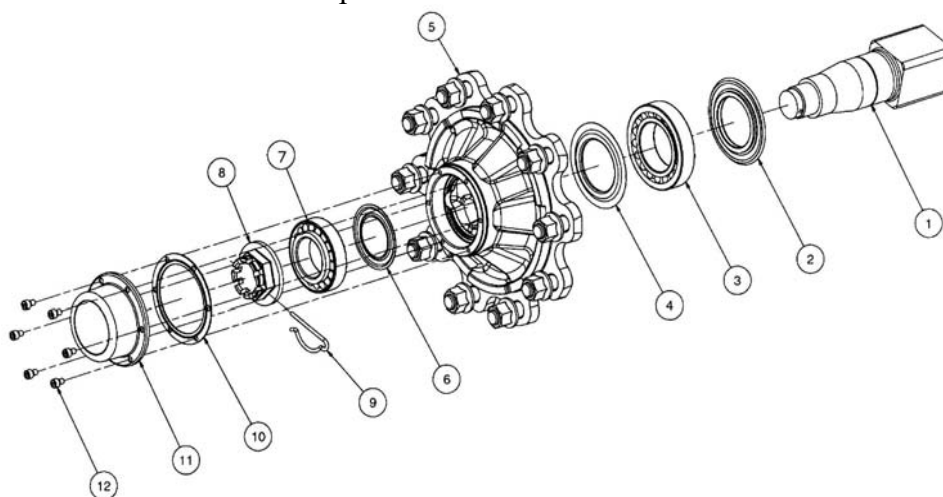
Схема регулировки подшипников ступиц колес полуприцепа
